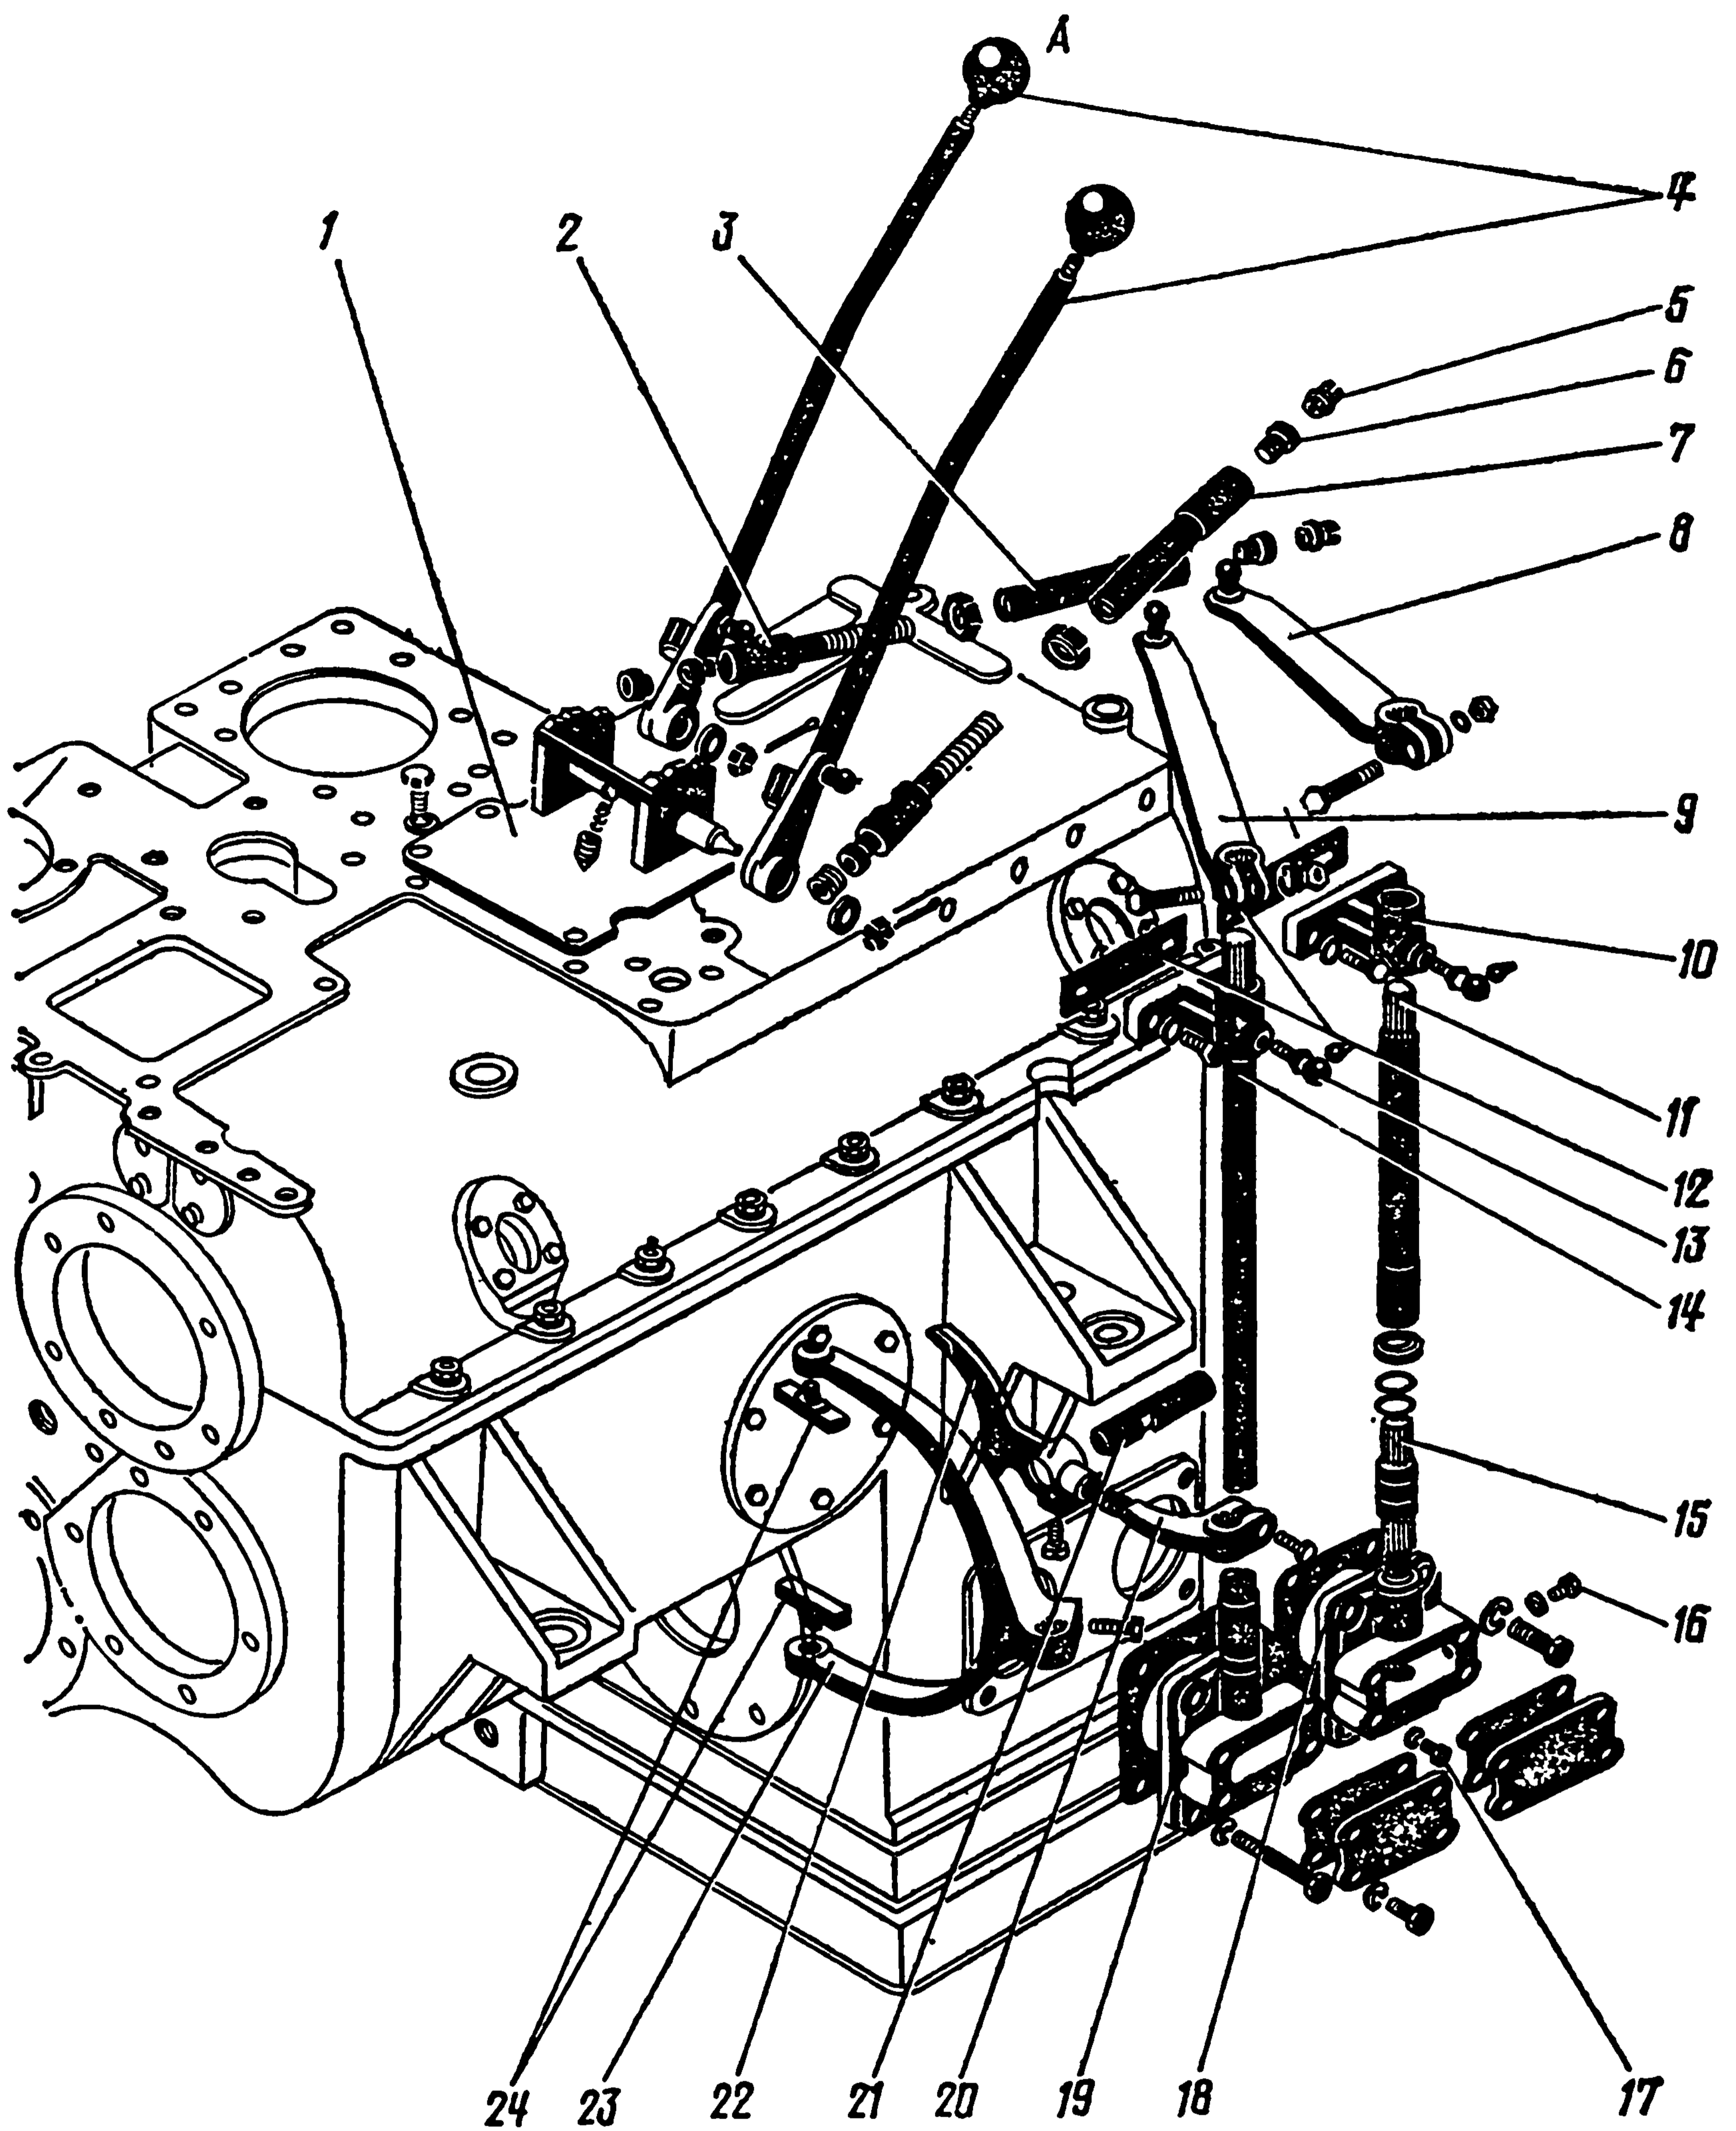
Привод управления зубчатыми муфтами раздаточного вала:
